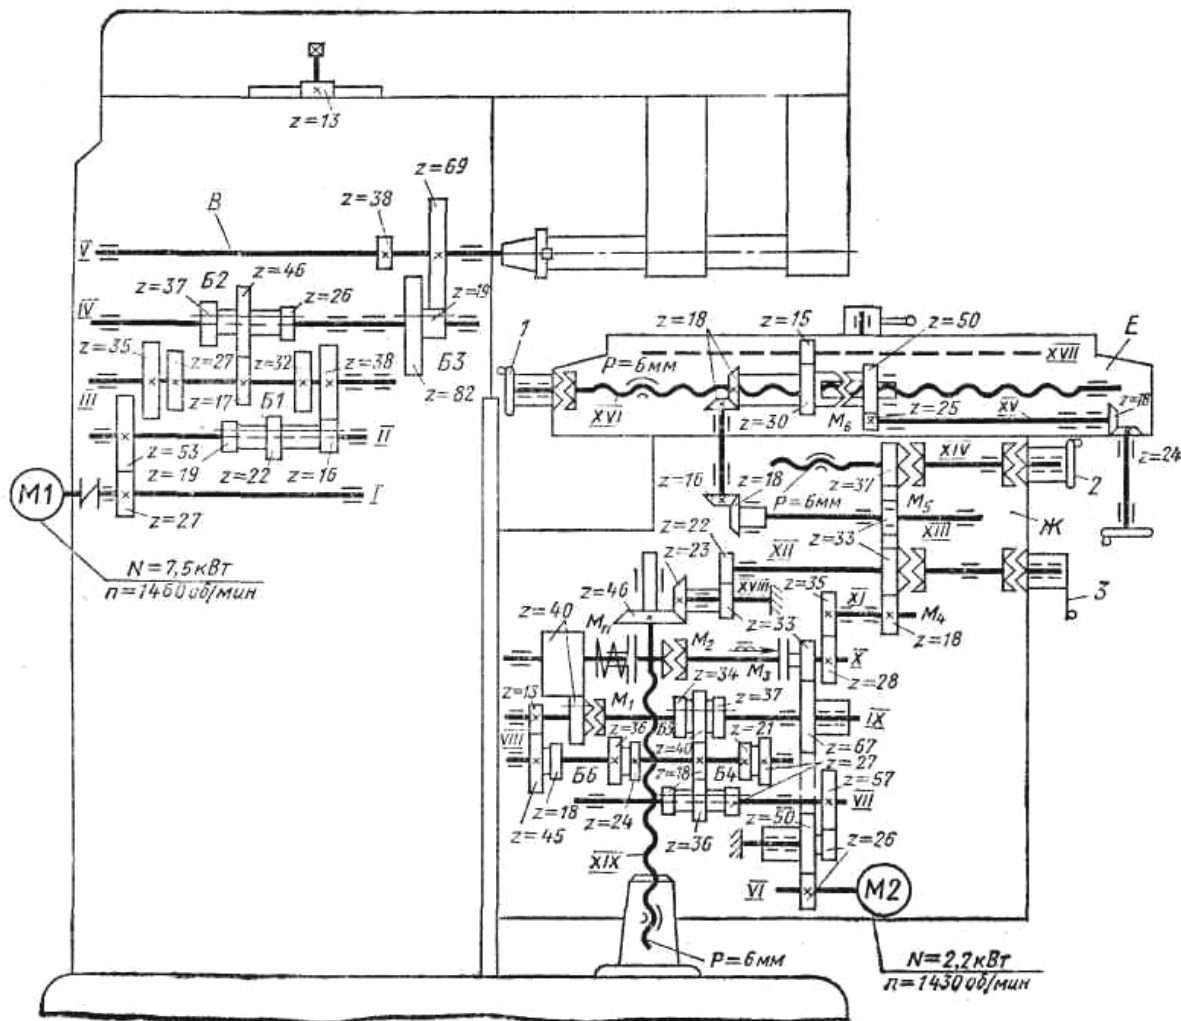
Кинематическая схема горизонтально-фрезерного станка модели 6P82
